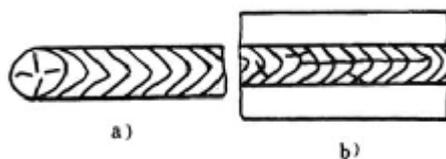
a) 弧坑裂纹 b) 焊缝热裂纹
